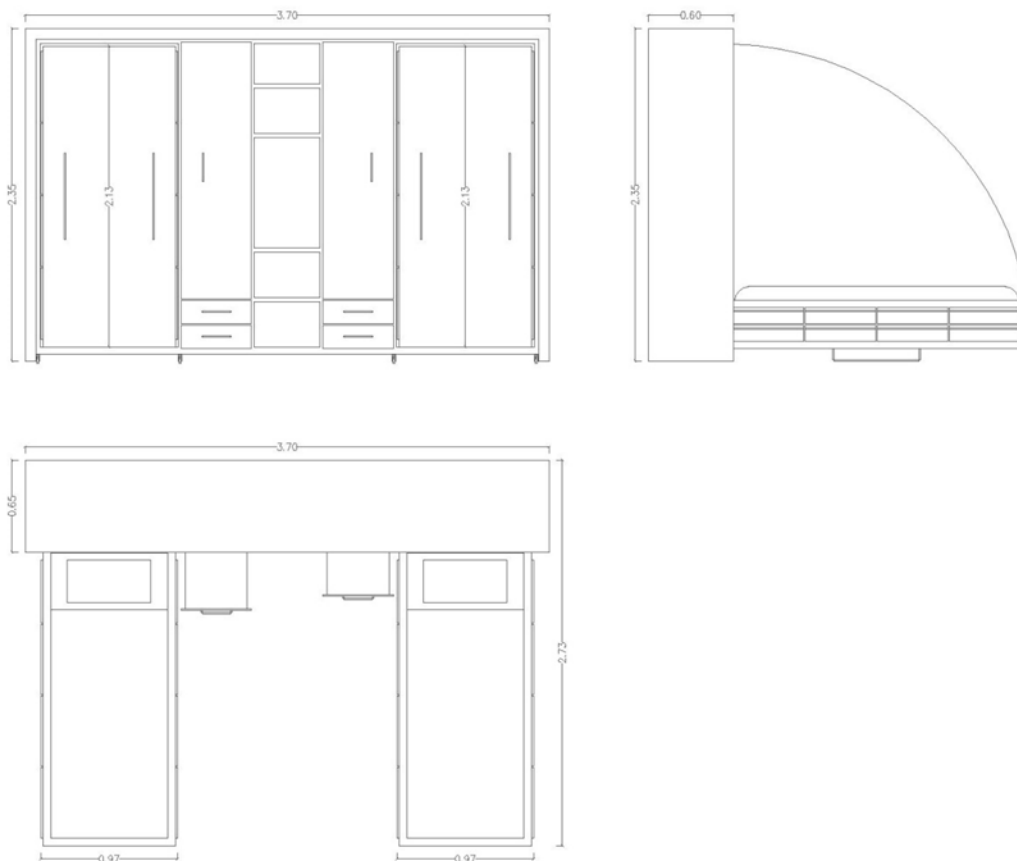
Duas camas de solteiro com roupeiro e mesas-de-cabeceira. Planta e alçados.
